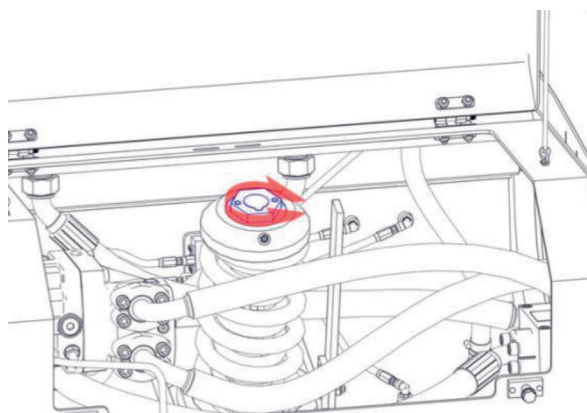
Регулировка зазора: снять крышку. Снять крышку блока, удалив болты М12 с наружной стороны корпуса дробильного ковша.
